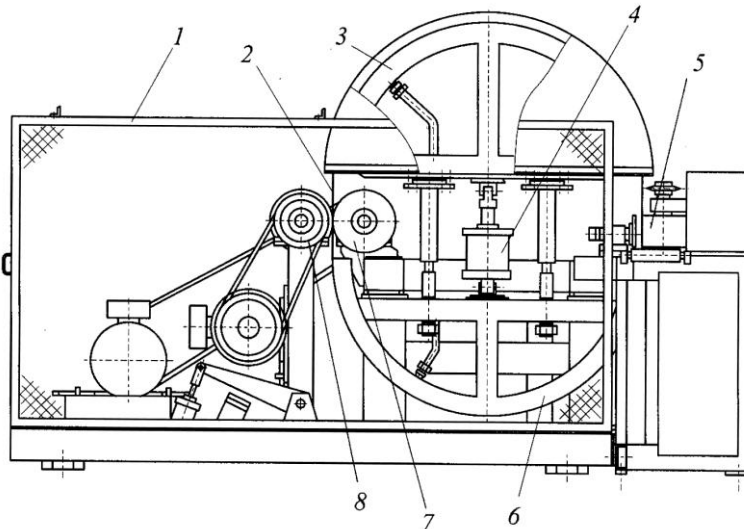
Ленточнопильный станок с пилой, движущейся по криволинейным аэростатическим направляющим: 1 – ограждение; 2 – пила; 3, 6 – верхняя и нижняя криволинейные аэростатические направляющие; 4 – механизм натяжения пилы; 5 – механизм подачи; 7, 8 – приводные фрикционные колеса
